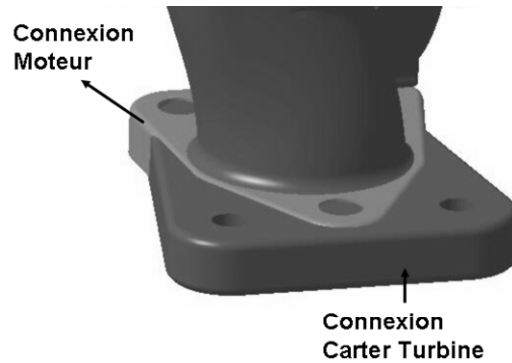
Interface moteur – turbocompresseur (coté carter turbine)
